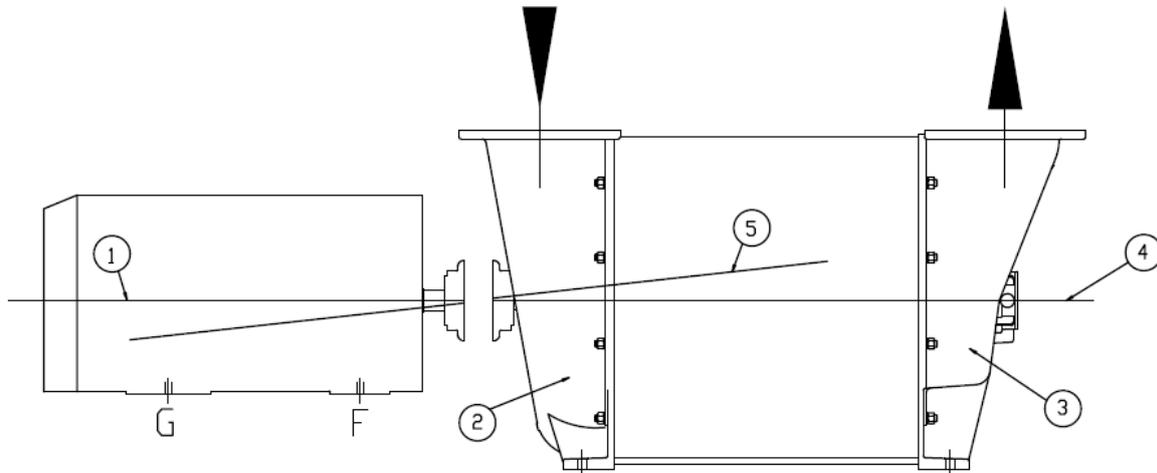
Calcolo dell'adeguamento con il motore sul lato di aspirazione
